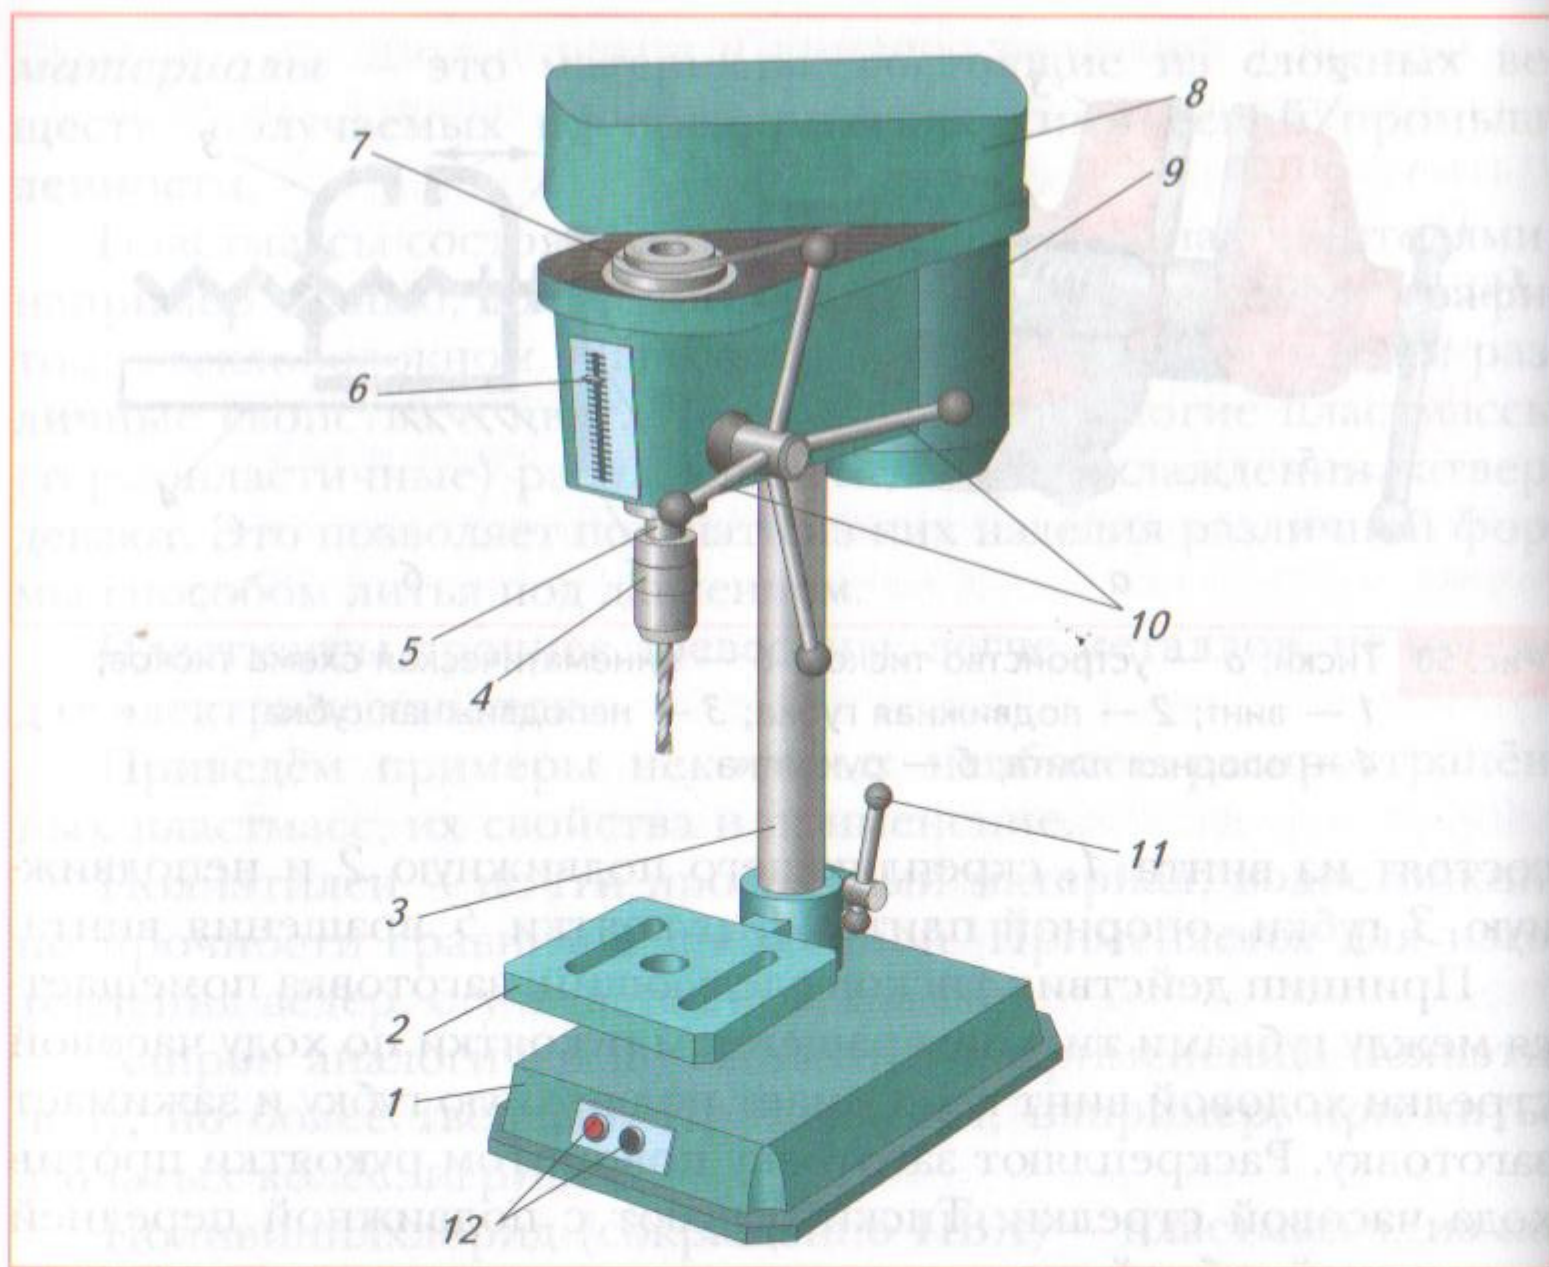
Устройство сверлильного станка: 1 — основание; 2 — рабочий стол; 3 — колонна; 4 — патрон со сверлом; 5 — рабочий вал; 6 — указатель со шкалой глубины сверления; 7 — клиноремённая передача; 8 — защитный кожух; 9 — электродвигатель; 10 — рукоятки подачи сверла; 11 — стопор; 12 — кнопки включения и выключения
